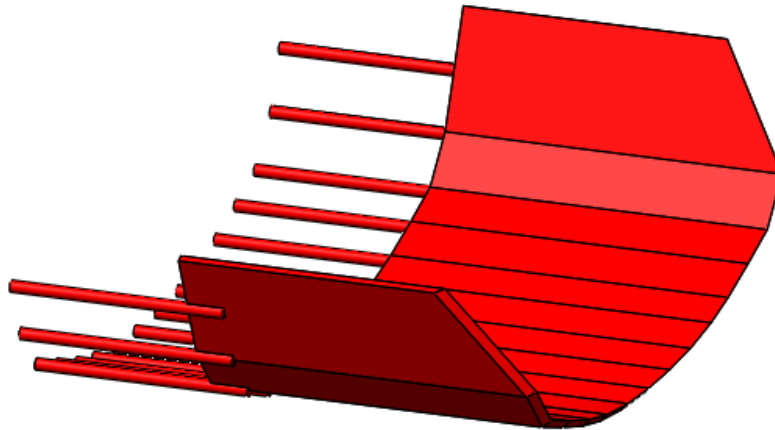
Vue en perspective du soc sur SolidWorks
